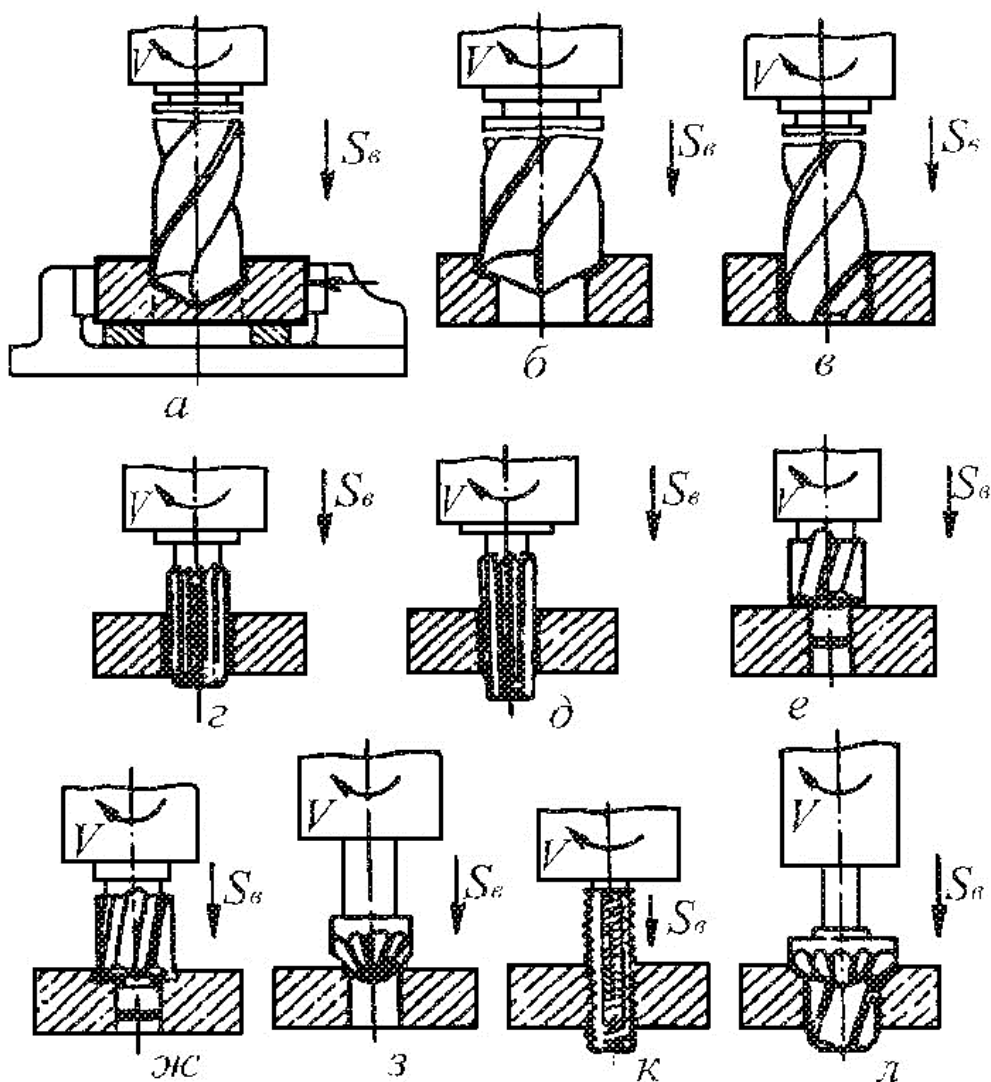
Схеми обробки заготовок на свердлильних верстатах
